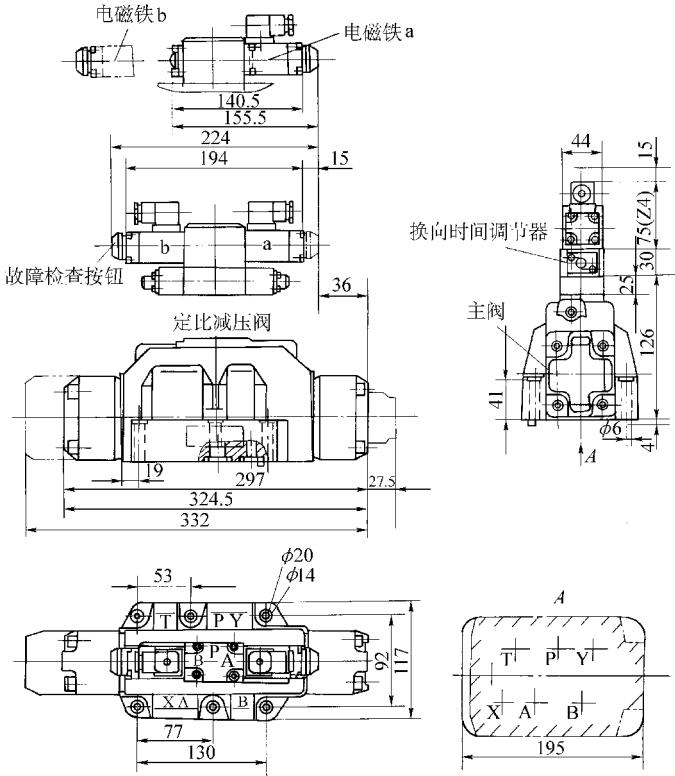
4WEH25 型电液换向阀外形尺寸图
